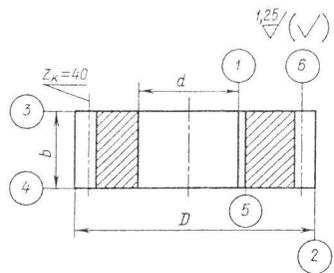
Деталь типа цилиндрического зубчатого колеса
